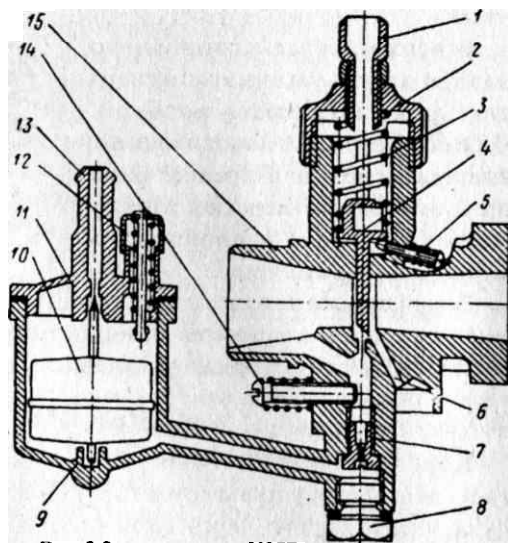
Карбюратор К35В: 1 - упор; 2 - крышка корпуса; 3 - пружина; 4 - дроссель; 5 - винт упора дросселя; 6 - корпус; 7 - главный жиклер; 8 - пробка жиклера; 9 - поплавковая камера; 10 - поплавок; 11 - крышка поплавковой камеры; 12 - уплотнитель поплавка; 13 - топливный штуцер; 14 - винт регулировки качества смеси; 15 - корпус
